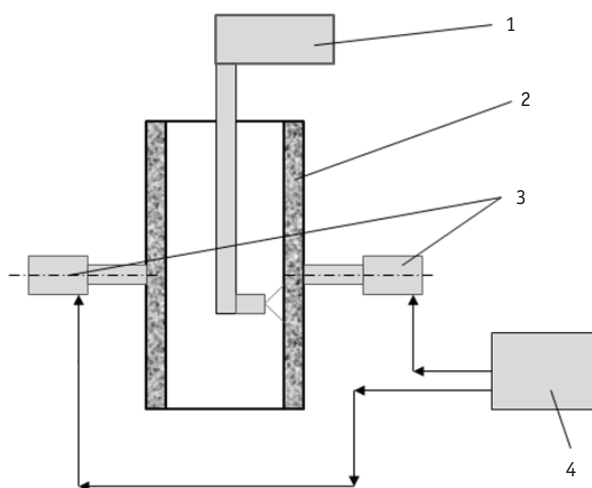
Схема устройства ультразвуковой обработки наплавки трубопровода: 1 – сварочный автомат; 2 – труба; 3 – ультразвуковые преобразователи; 4 – блок ультразвуковых генераторов
